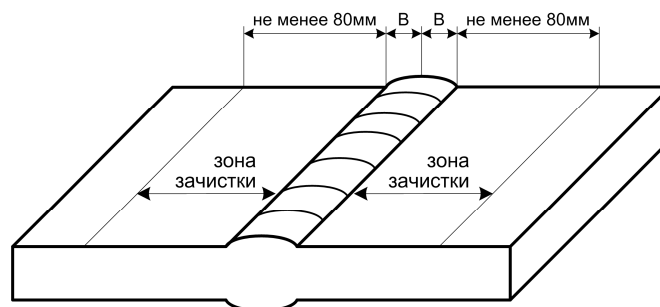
Подготовка стыковых соединений к контролю.
